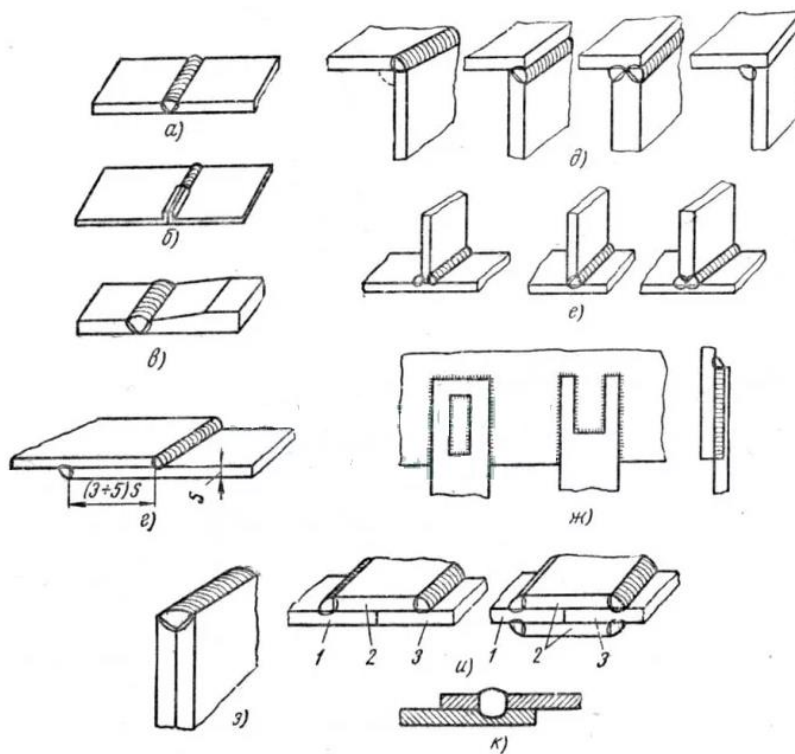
Основные виды сварных соединений:
